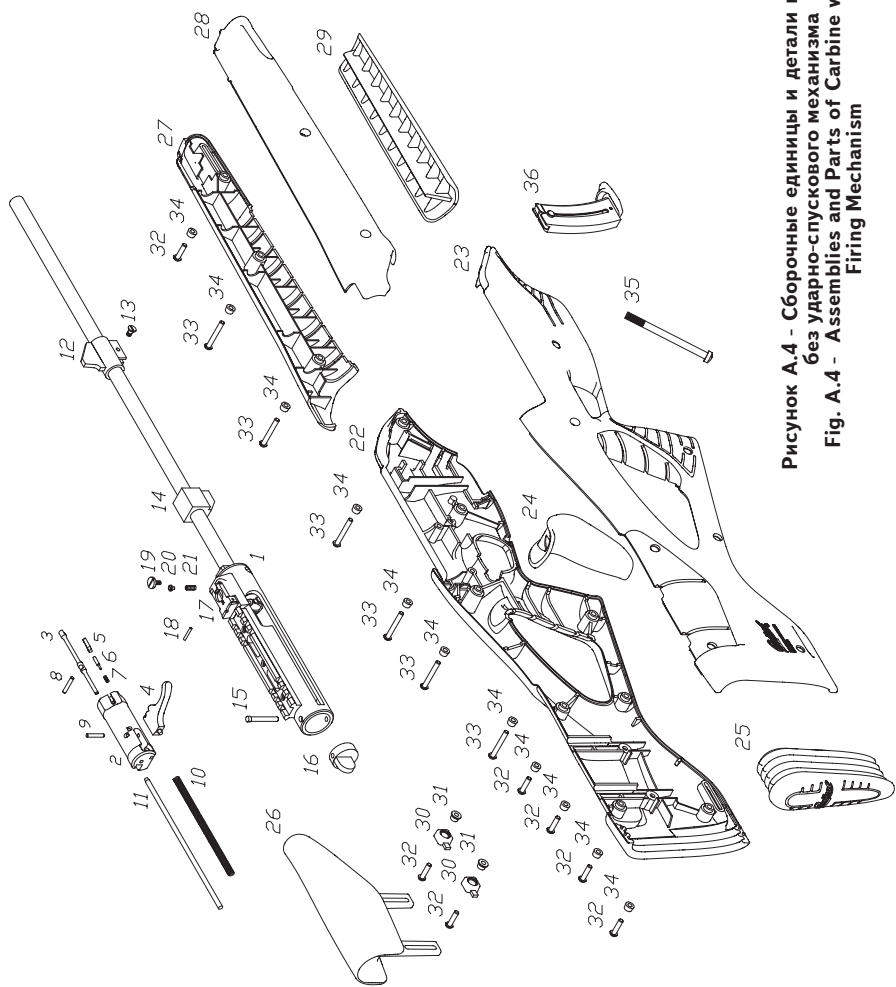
Сборочные единицы и детали карабина без ударно-спускового механизма
